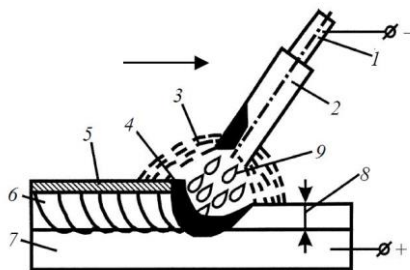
Схема ручного дугового зварювання металевим електродом з покриттям: 1 – металевий стрижень; 2 – покриття електрода; 3 – газова атмосфера дуги; 4 – зварювальна ванна; 5 – затверділий шлак; 6 – метал шва; 7 – основний метал; 8 – глибина проплавлення; 9 – краплі розплавленого електродного металу
